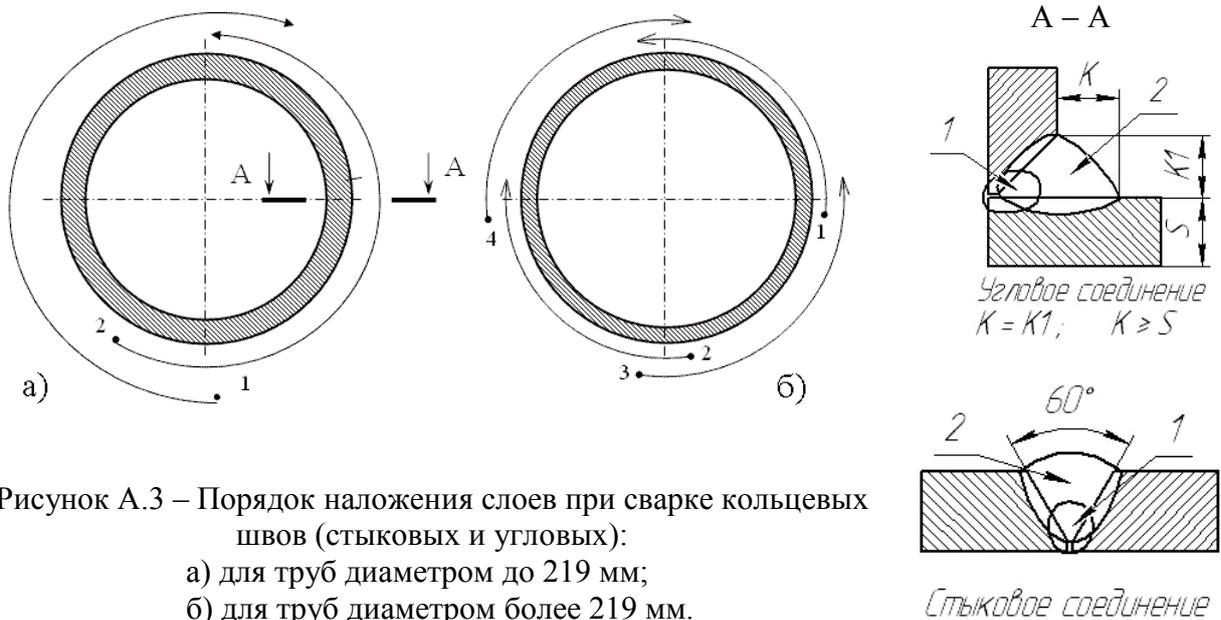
Порядок наложения слоев при сварке кольцевых швов (стыковых и угловых):
